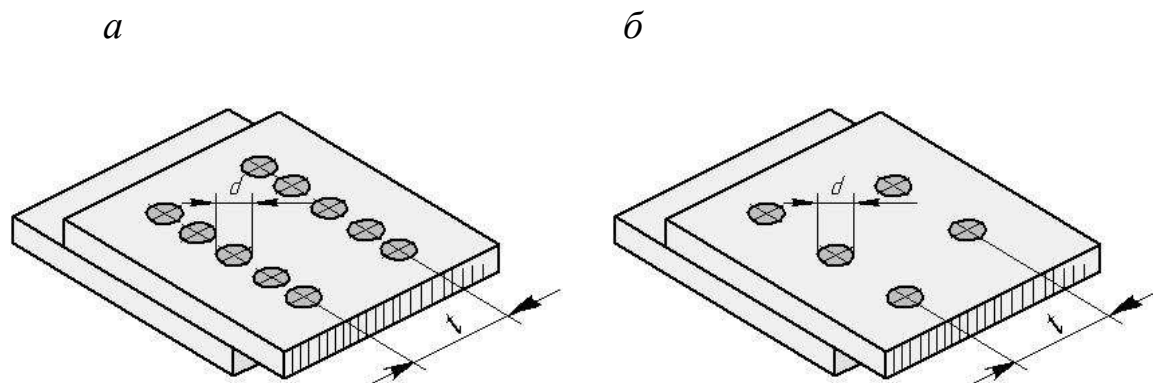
Точечные сварные швы: *a* – цепной; *б* – шахматный
